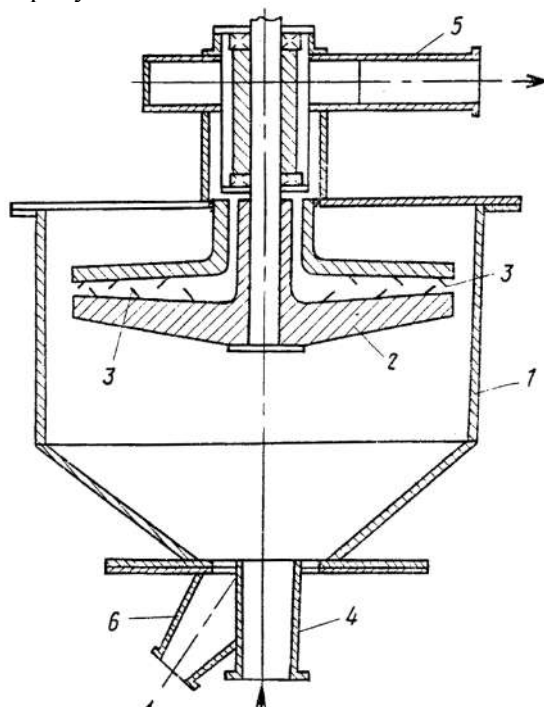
Центробежный классификатор: 1 – корпус; 2 – ротор; 3 – конусные полки; 4 – патрубок ввода воздуха с исходным материалом; 5, 6 – патрубки вывода продуктов разделения.
